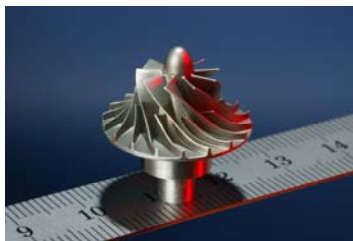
Das Laufrad, einer der Bestandteile des Turbokompressors, mit einem Durchmesser von 20 Millimetern.
